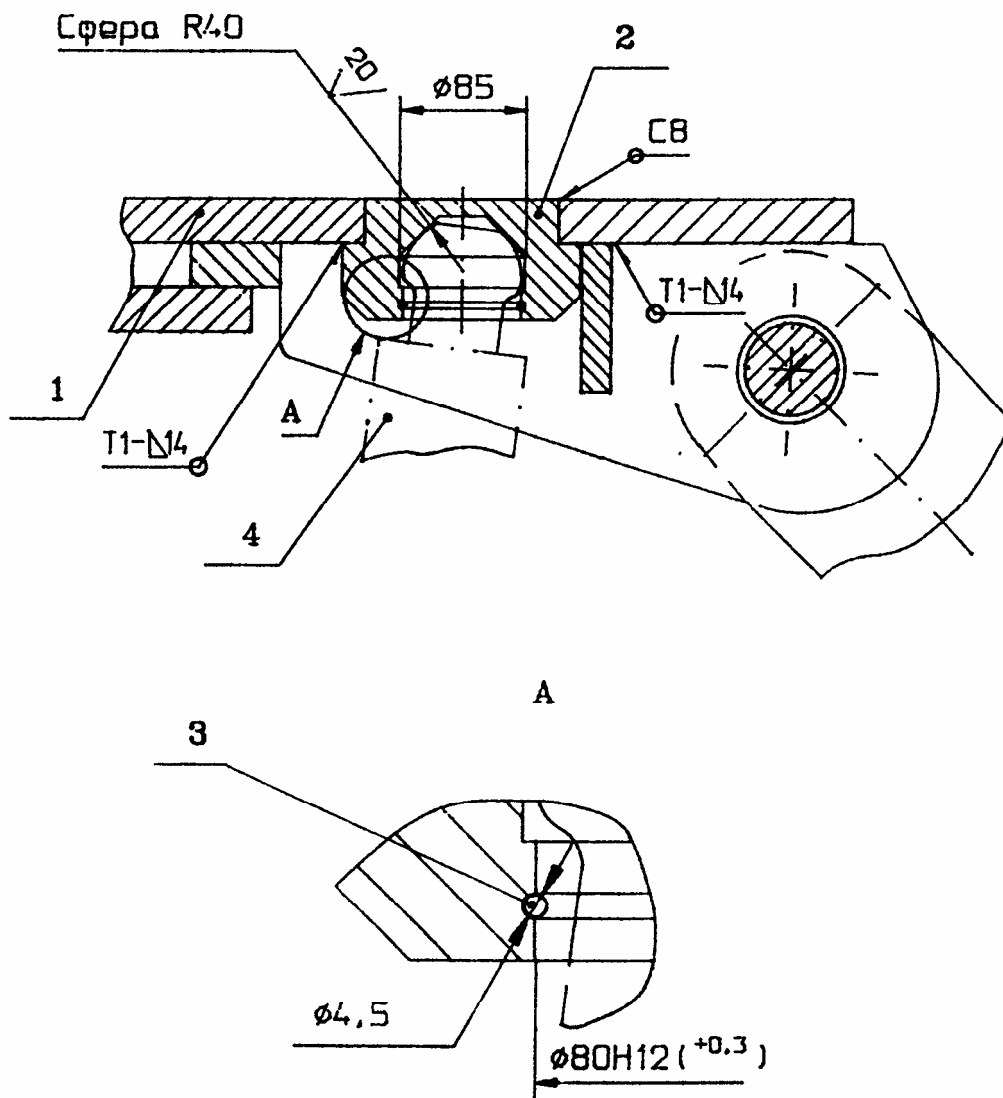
Соединение перекрытия секции крепи КД80 с гидростойкой
